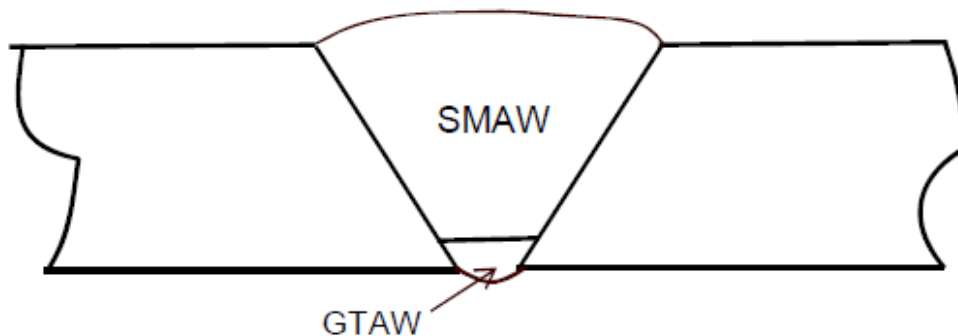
Croquis de la soldadura longitudinal y circunferencial. Fuente: Hispánica Calderería.
